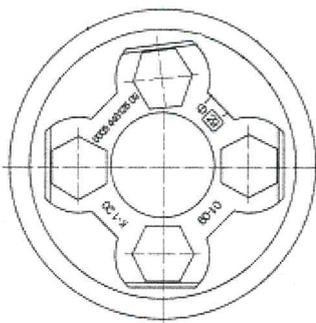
Внешние отличительные признаки буксового узла с подшипником кассетного типа в габаритных размерах 130x230x150 мм, 130x250x160мм и 150x250x160 мм торговой марки BRENCO (ЕПК- BRENCO) под адаптер для крепления четырьмя болтами М20
